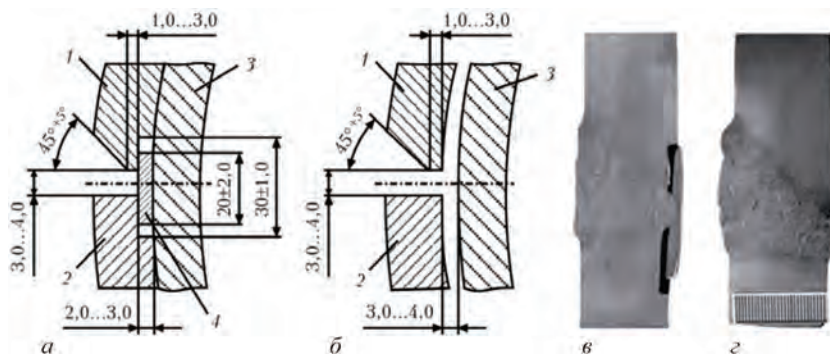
Поздовжні стикові з'єднання конструктивних елементів, підсилювальних елементів: *а* — обробка крайок для зварювання з підкладною пластиною; *б* — обробка крайок для зварювання «на вазі»; *в* — макрошліф з'єднання з підкладною пластиною (дріт DW-A55); *г* — макрошліф з'єднання, виконаного дротом Sv-08Г2С «на вазі»; 1, 2 — стінка відповідно верхнього та нижнього підсилювального елемента; 3 — стінка газопроводу; 4 — підкладна пластина
